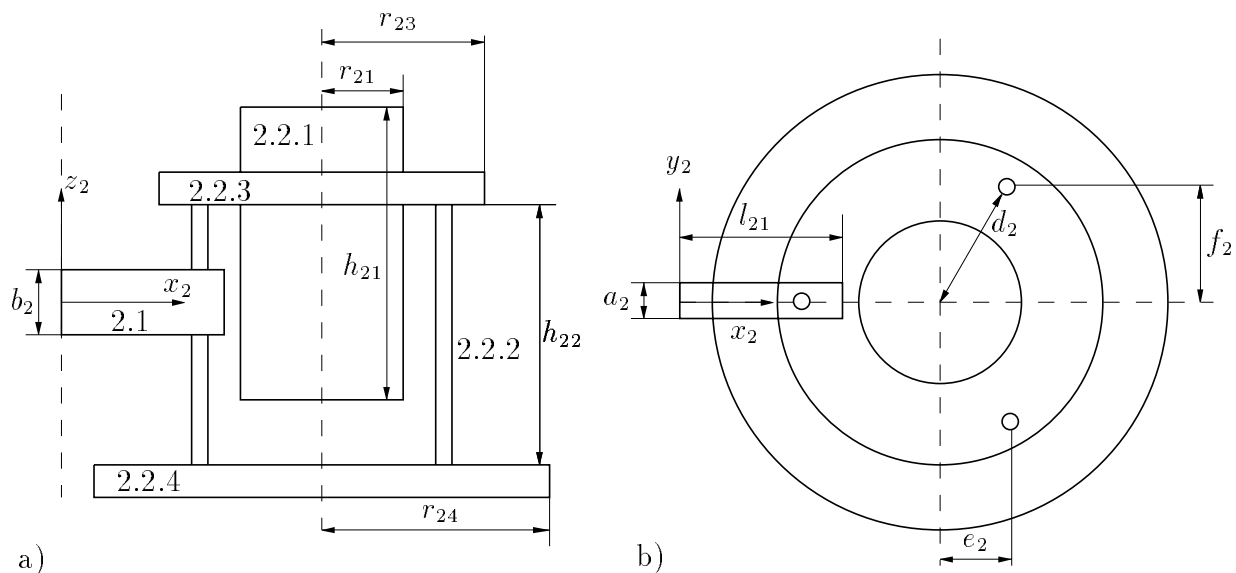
Glied 2 a) Seitenansicht; b) Draufsicht
